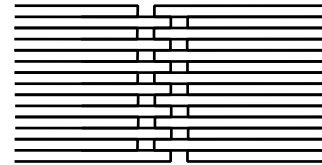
Skládání překlátováním pod úhlem 45° [12]
